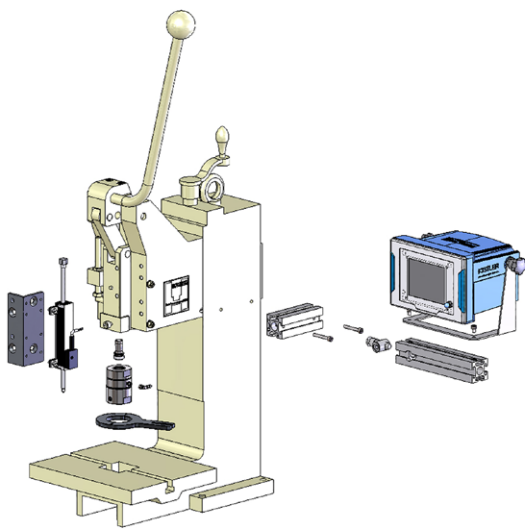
Explosionszeichnung Einzelteile Retrofitset für Handpressen
